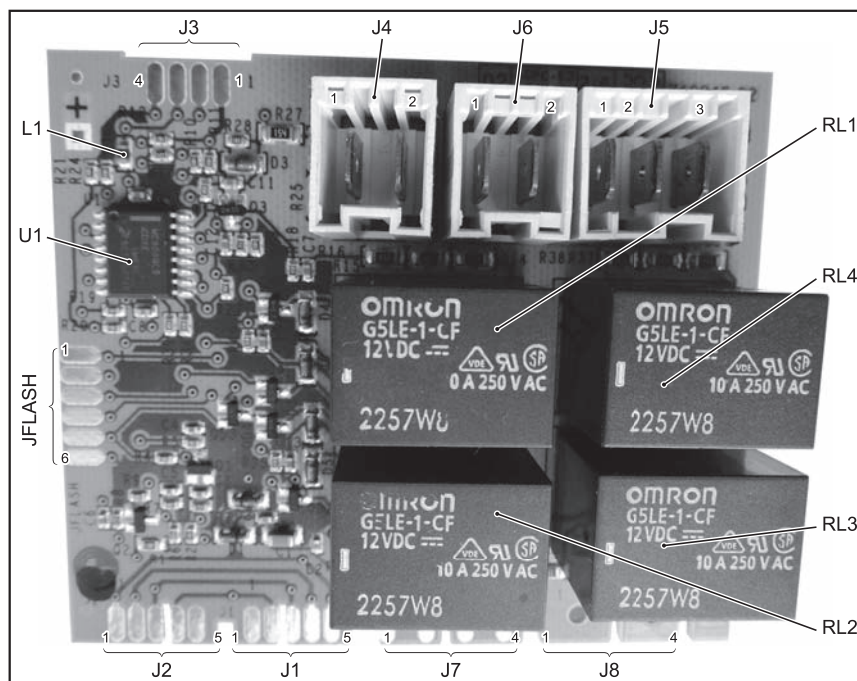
Внешний вид ЭМ 1324479021, его основные компоненты и соединители
